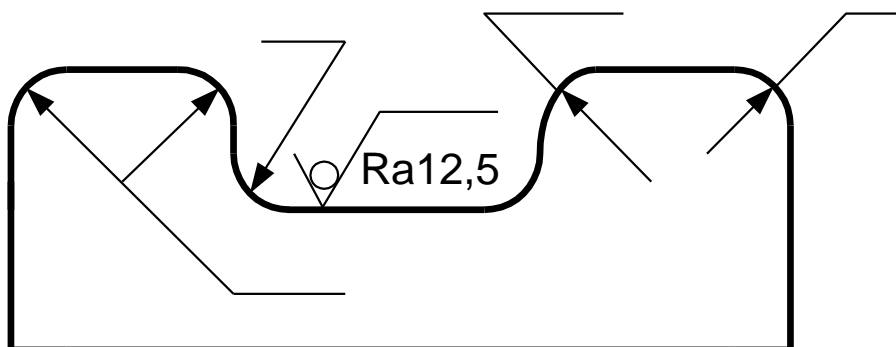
Обозначение шероховатости поверхностей, плавно переходящих друг в друга
